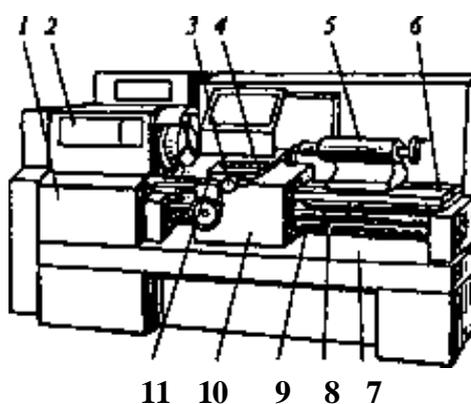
Токарно-винторезный станок :1 — коробка подач; 2 — передняя (шпиндельная) бабка; 3 — поперечные салазки; 4 — резцовая каретка; 5 — задняя бабка; 6 — направляющие; 7 — станина; 8 — ходовой винт; 9 — ходовой вал; 10 — фартук; 11 — суппорт инструментальный
